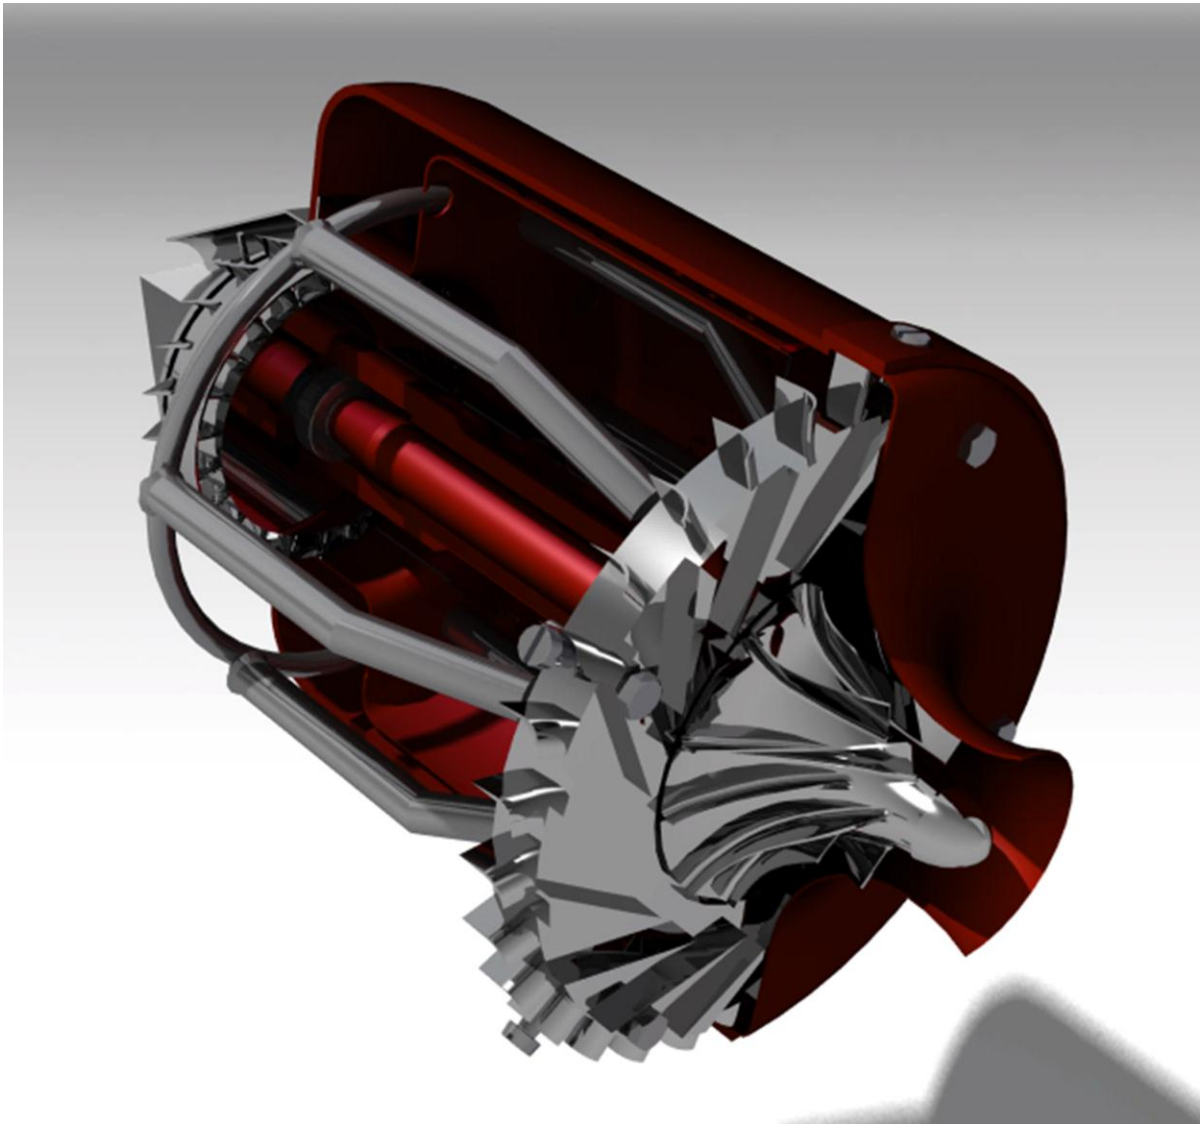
Mini Turborreactor GMMO-1524-A.
